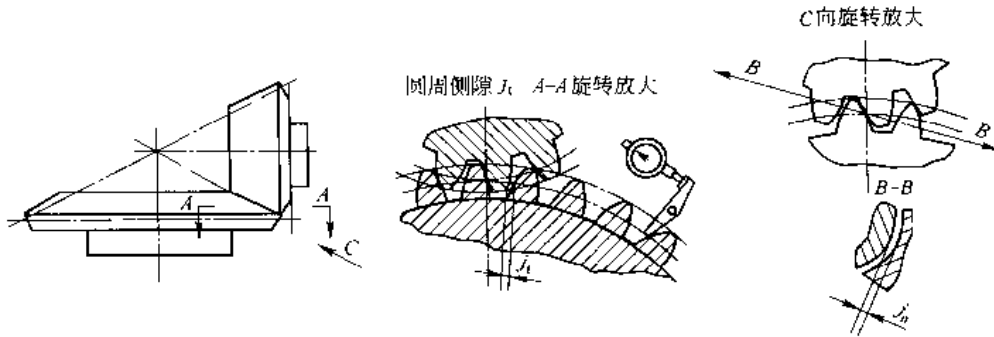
测量锥齿轮、准双曲面齿轮的侧隙
